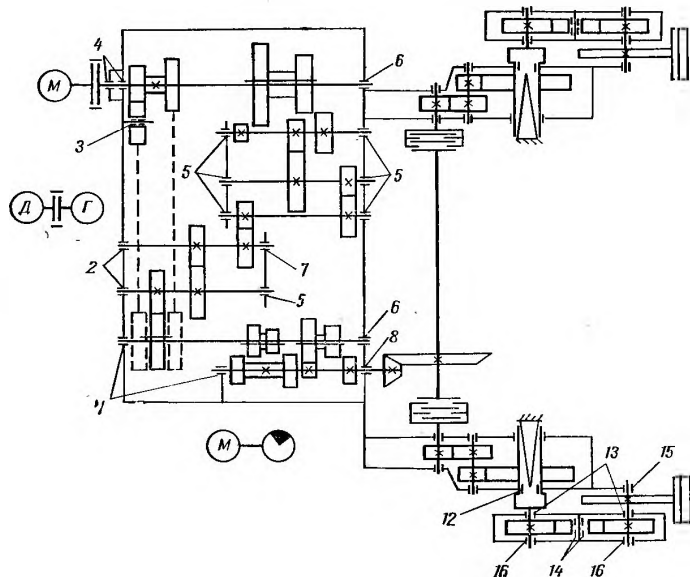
Кинематическая схема тягача экскаватора ЭТР231
